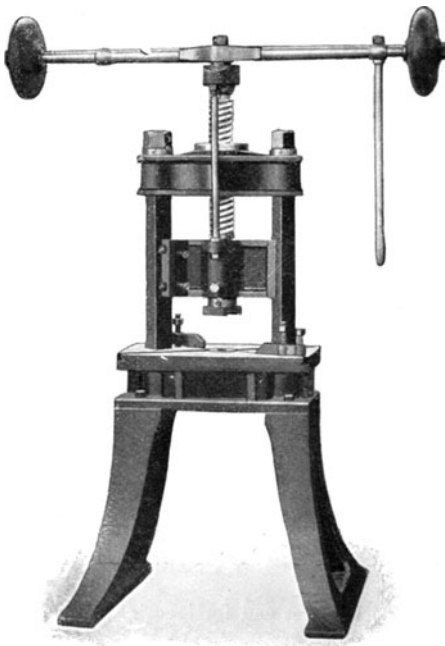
Spindelpresse zum Aufschweißen von Schnellstahl.
